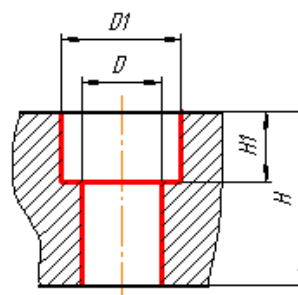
КТЭ цилиндрическое отверстие с цековкой сквозное для поверхностей №36, 38
